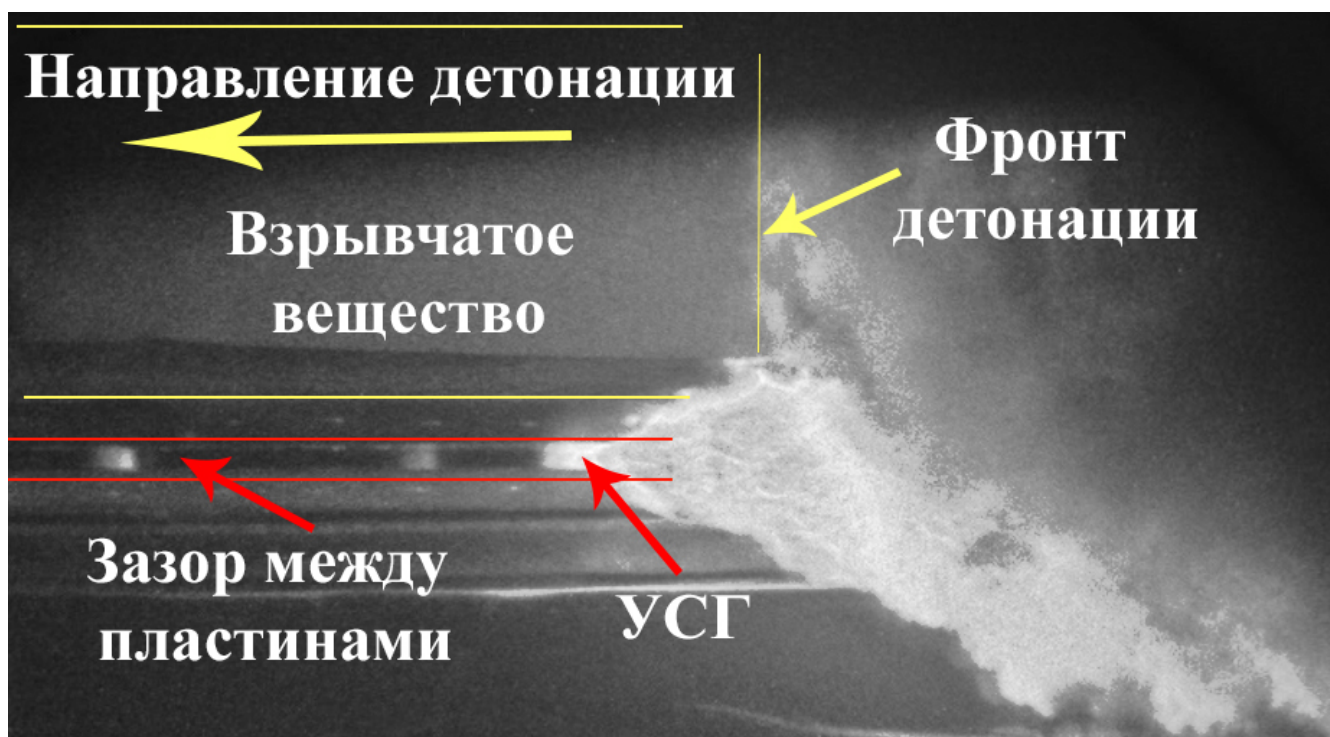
Фотокадр с изображением процесса сварки взрывом
